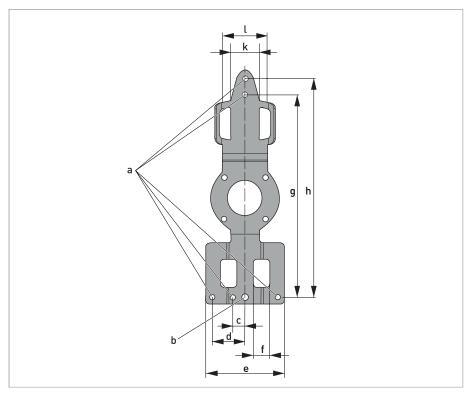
Dimensiones de la placa de montaje, versión de pared
